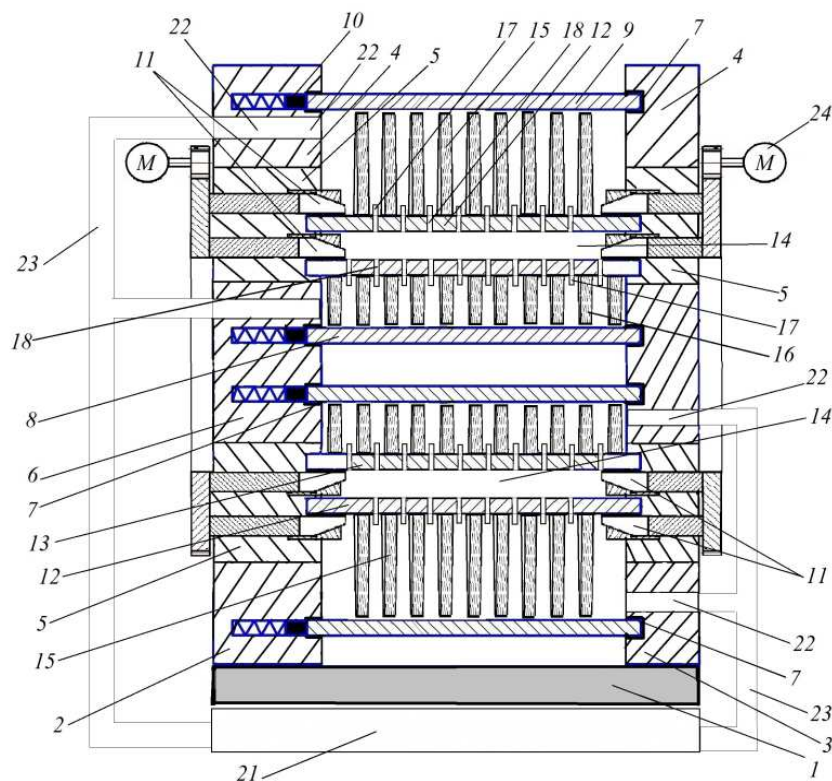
Вид устройства для осуществления способа пневмоабразивной обработки внутренних и наружных поверхностей трубных заготовок
